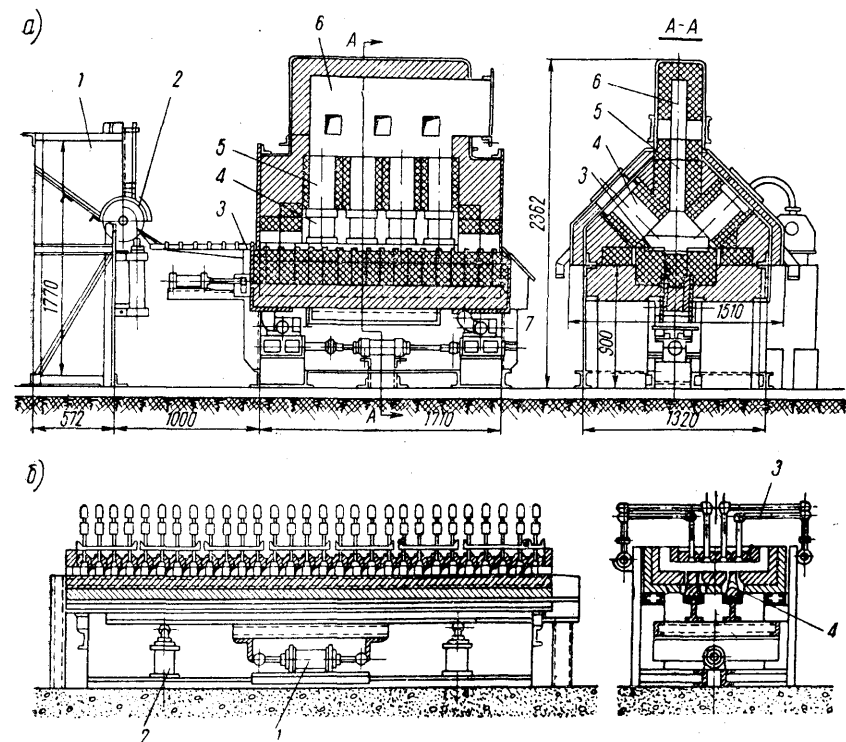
Печи скоростного нагрева заготовок под штамповку:
